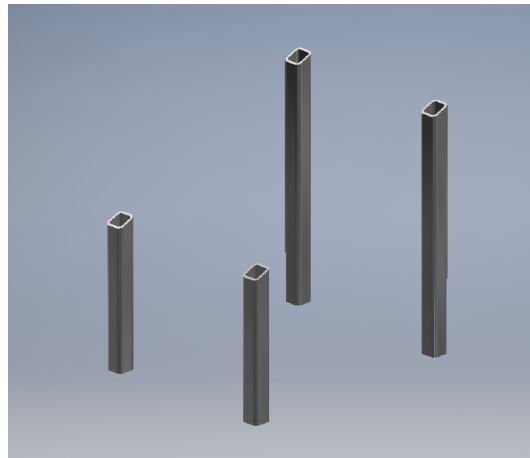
Modelo CAD columnas para rampa de caída inicial.
